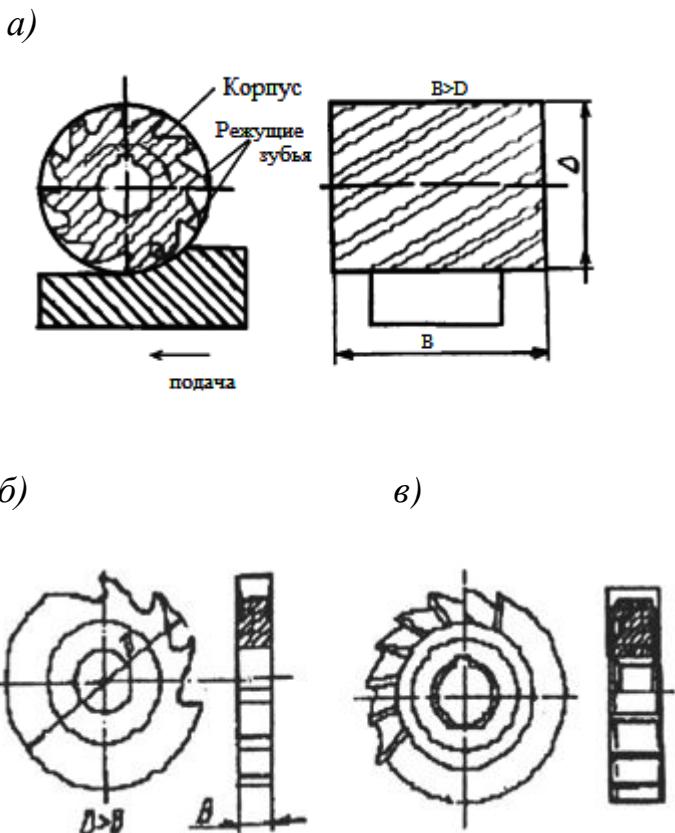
Осевые фрезы: а – цилиндрическая фреза;
